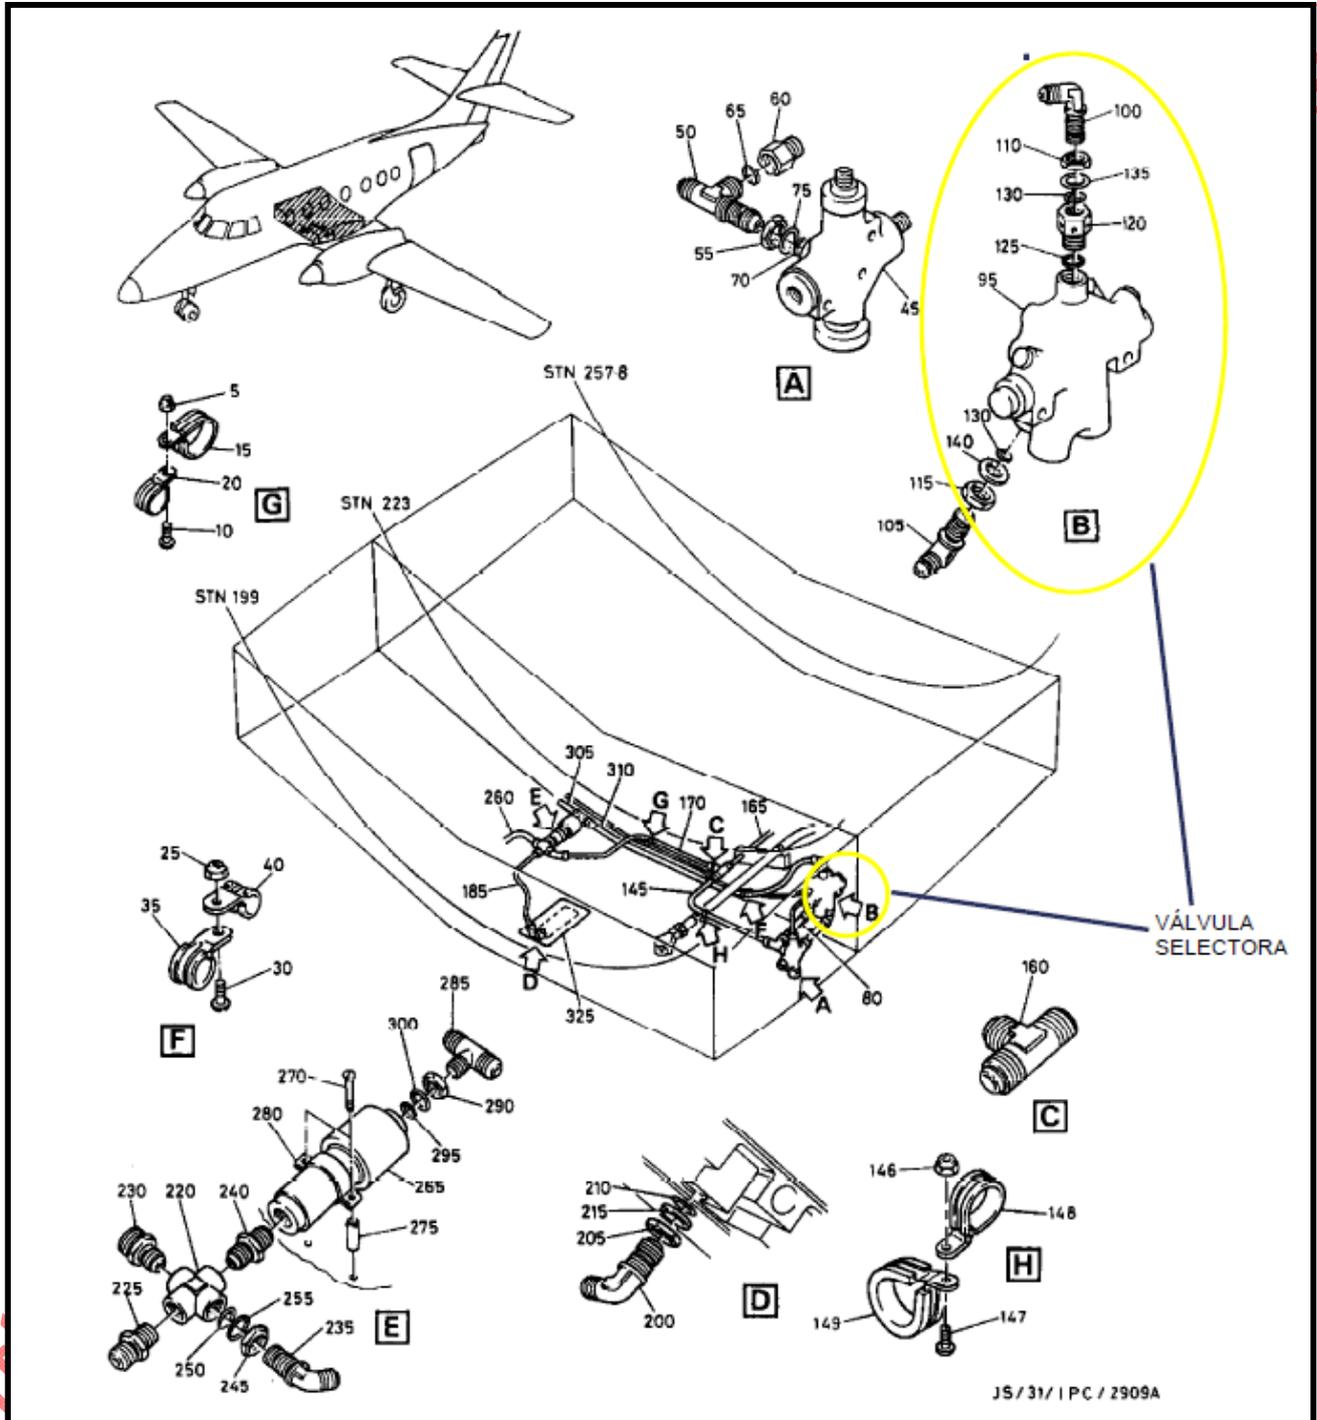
Hydraulic Instal-Centre Section, Landing Gear – AMM 29-10-00-40
